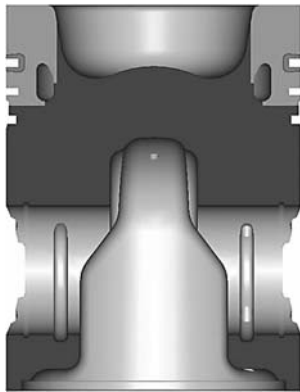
Сварной поршень с каналом охлаждения EB
